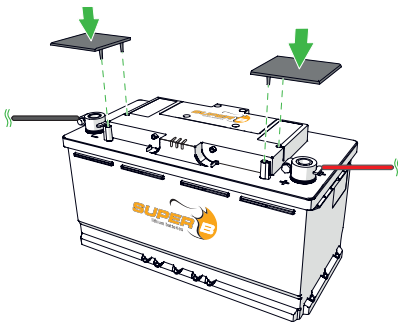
Plaats de beschermkappen over de aansluitklemmen. Super B levert geen beschermkappen voor auto's
